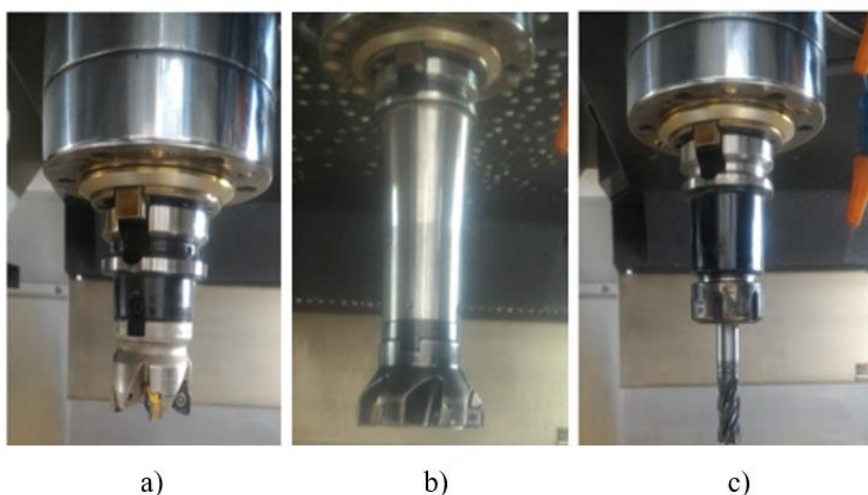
Ferramentas de fresagem: a) Fresa 50 mm; b) Roca 80 mm; c) Fresa de topo 16 mm.
